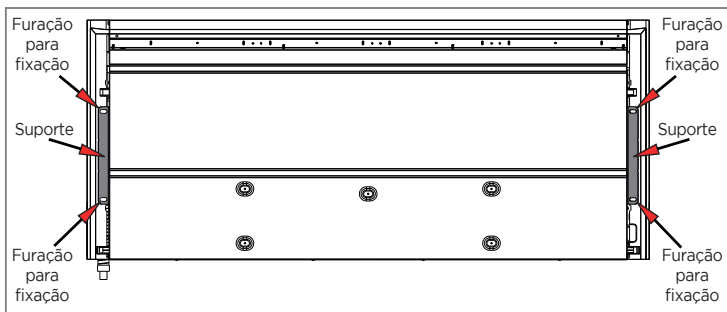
SUPORTES E FURAÇÃO PARA FIXAÇÃO
